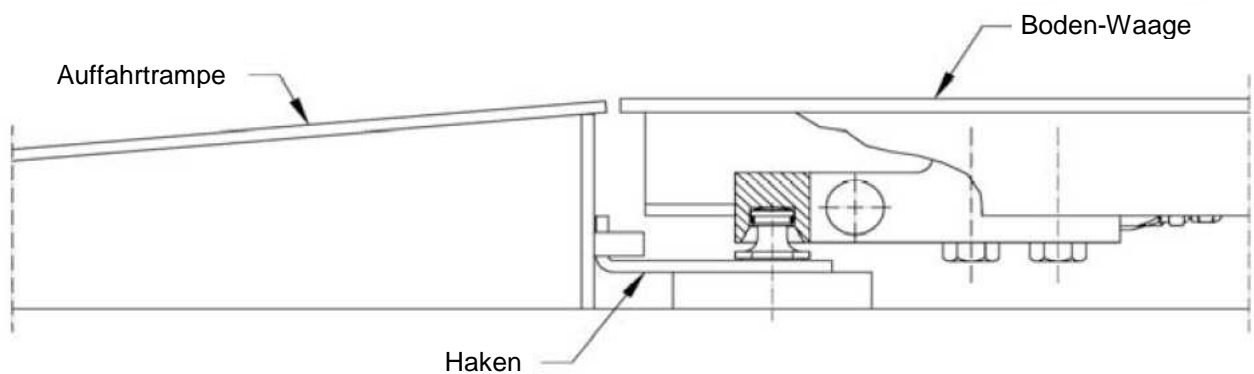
Lastfuß Typ 52-02 installiert unter einer Boden-Waage. Ein Haken ist am Lastbolzen montiert, um die Auffahrtrampe zu positionieren.
